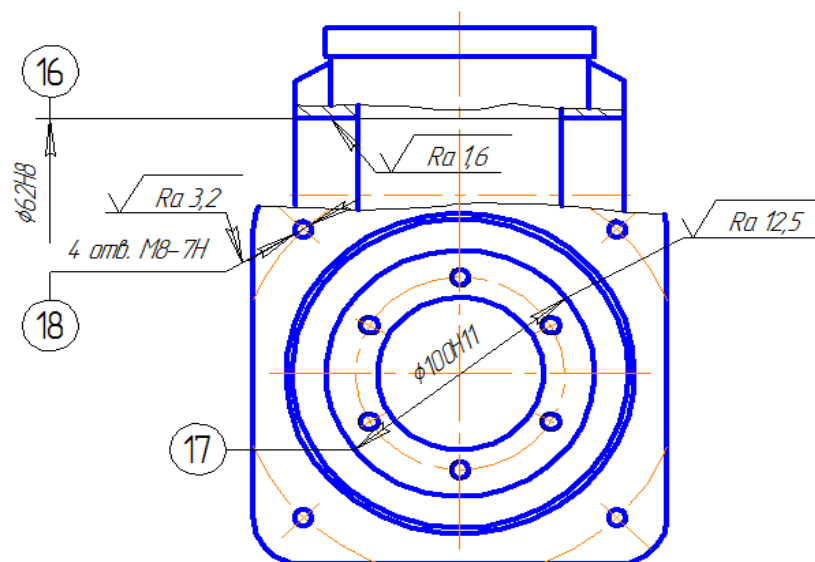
Эскиз детали «Корпус редуктора водяной помпы»
